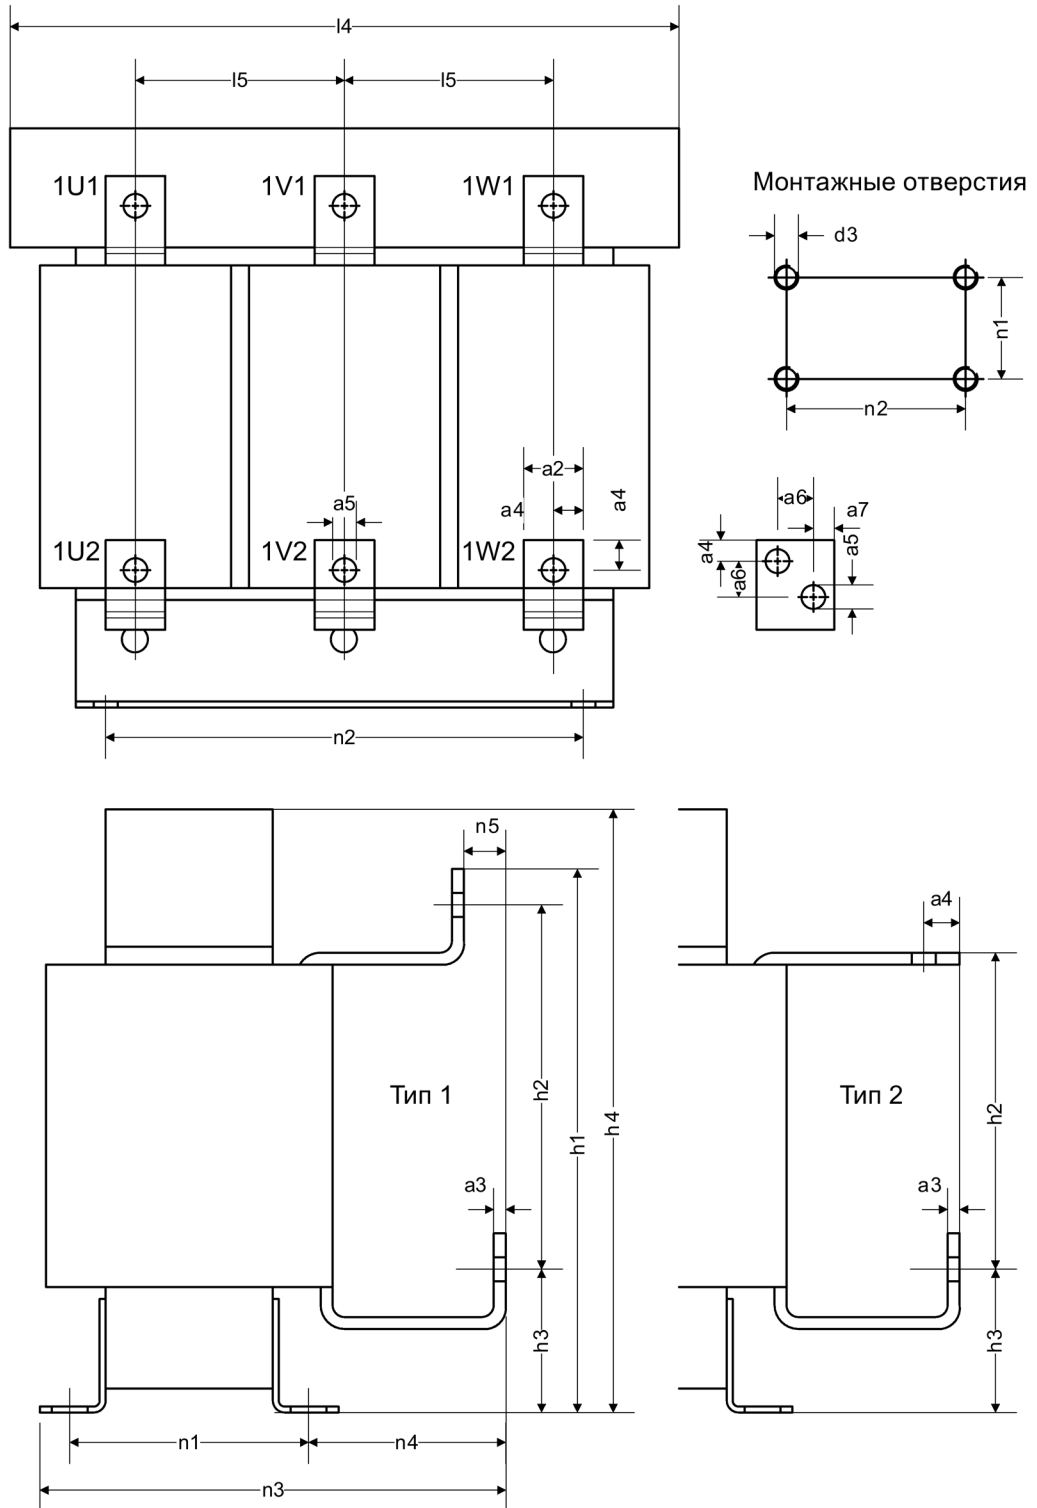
Габаритный чертёж дросселя двигателя
